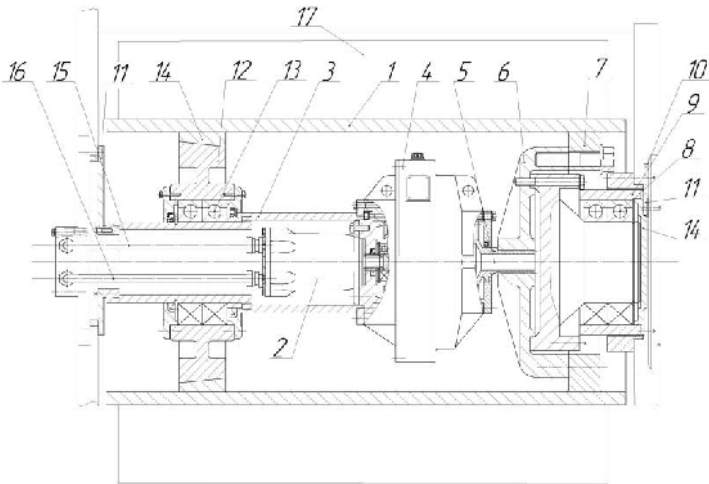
Робоче креслення фрезерного барабана машини холодного фрезерування доріг
